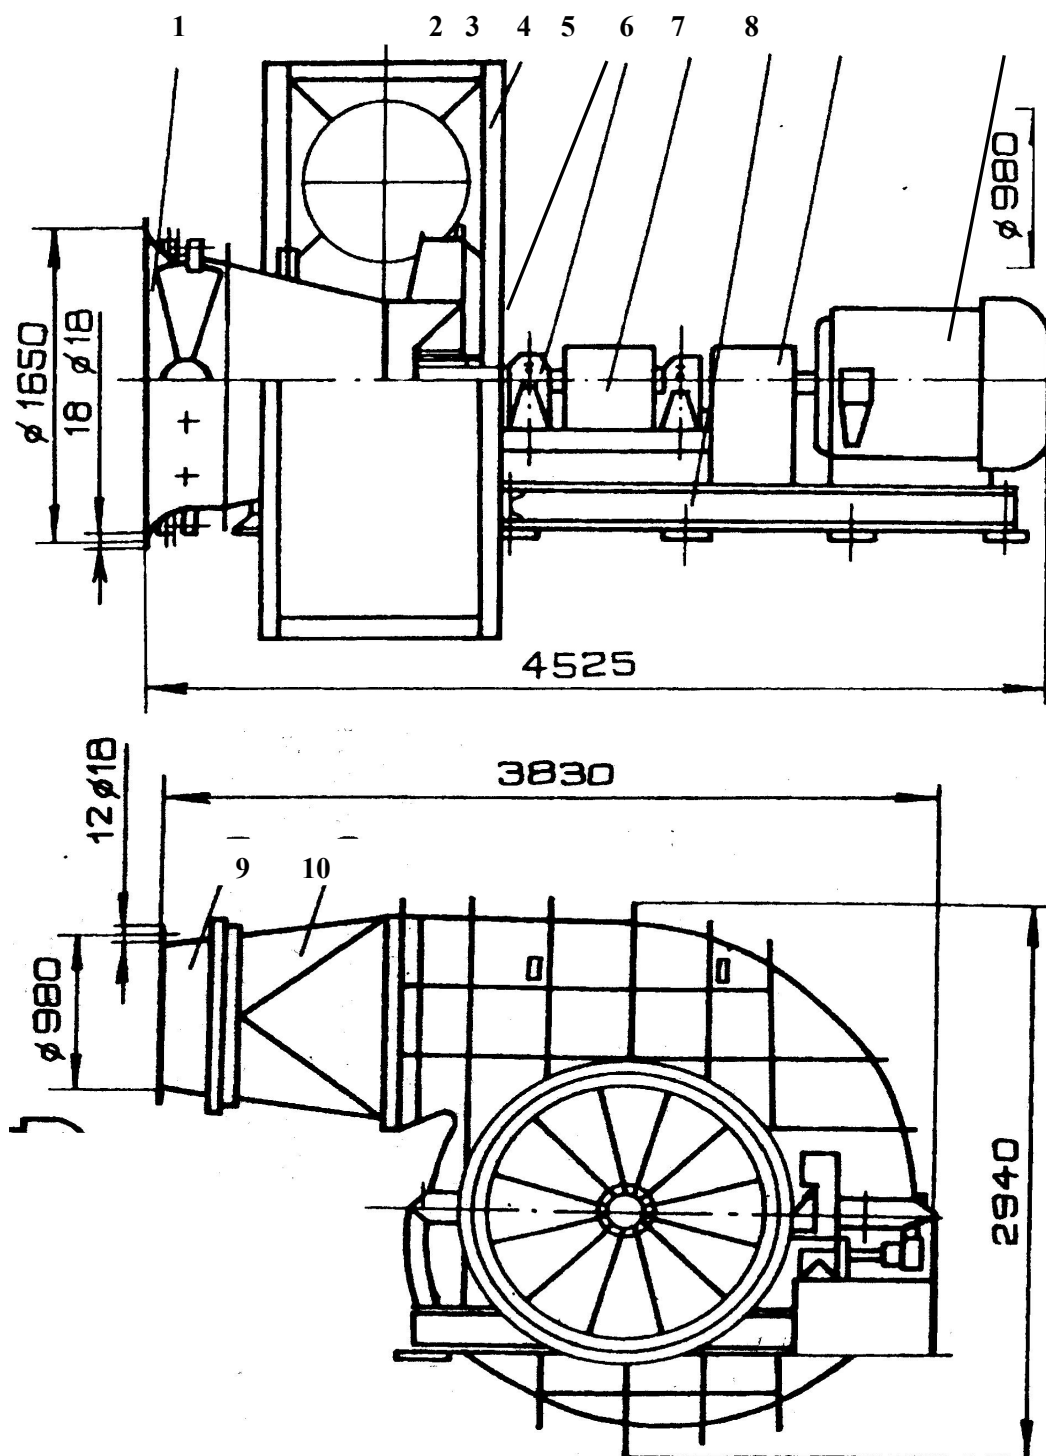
Прхідницький вентилятор ВЦП-16: 1 – направляючий апарат; 2 – корпус; 3 – ротор; 4 – підшипник; 5 – захисний кожух вала; 6 – рама; 7 – муфта в кожусі; 8 – електродвигун; 9 – патрубок трубопроводу; 10 - перехідник
